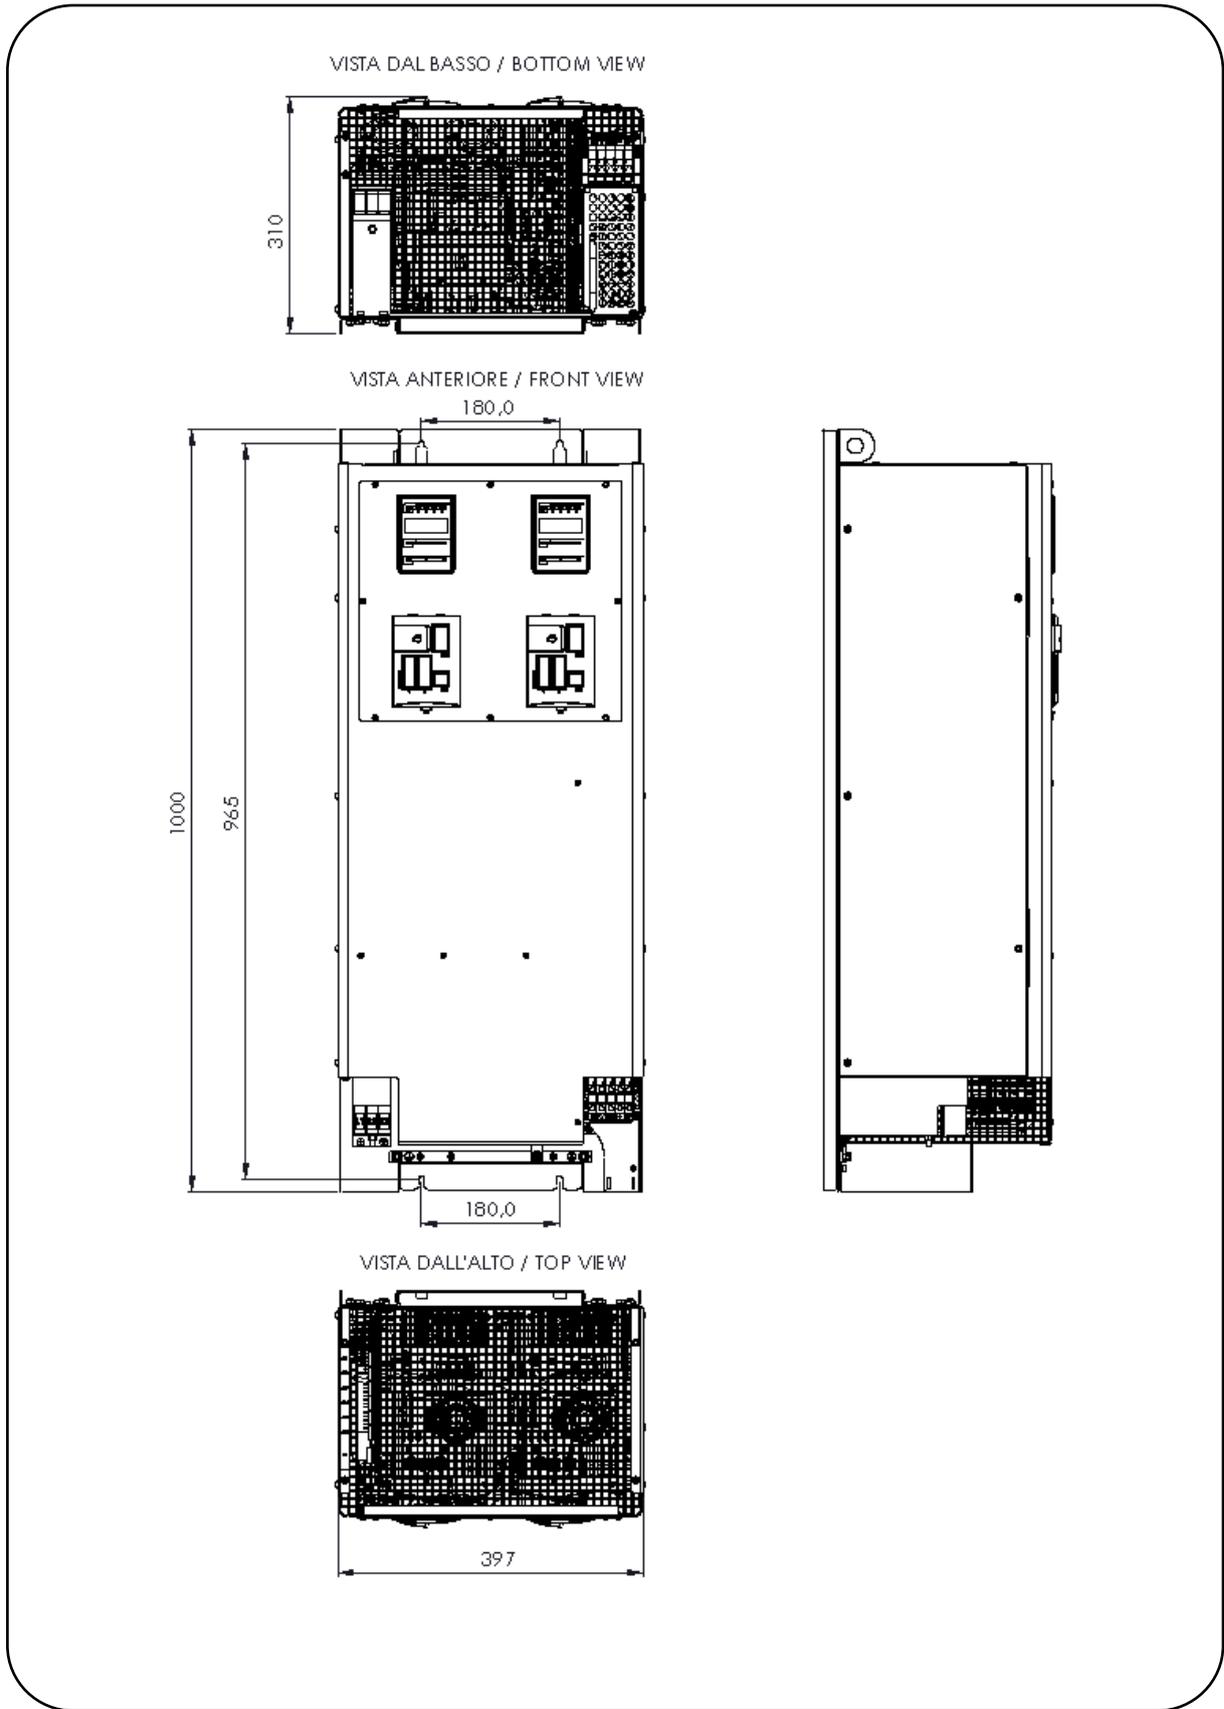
Dimensioni GE15 e GE20 / GE15 and GE20 Dimensions
